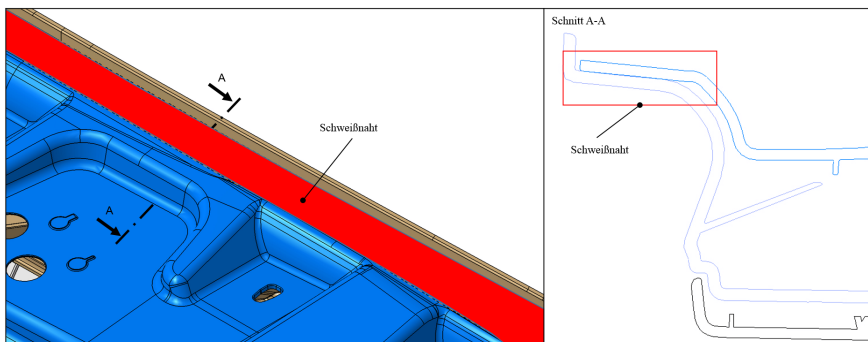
Schweißflansch mit Schnittansicht [104].
